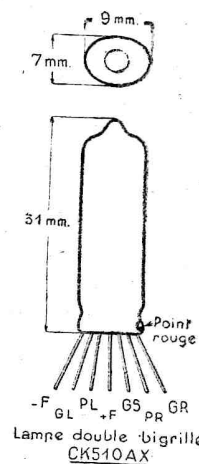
(ci-contre). — Dimensions et branchements du tube double bigrille CK 510 AX.
